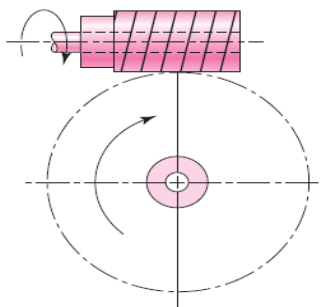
Engranajes de Tornillo sin fin o de Gusano
